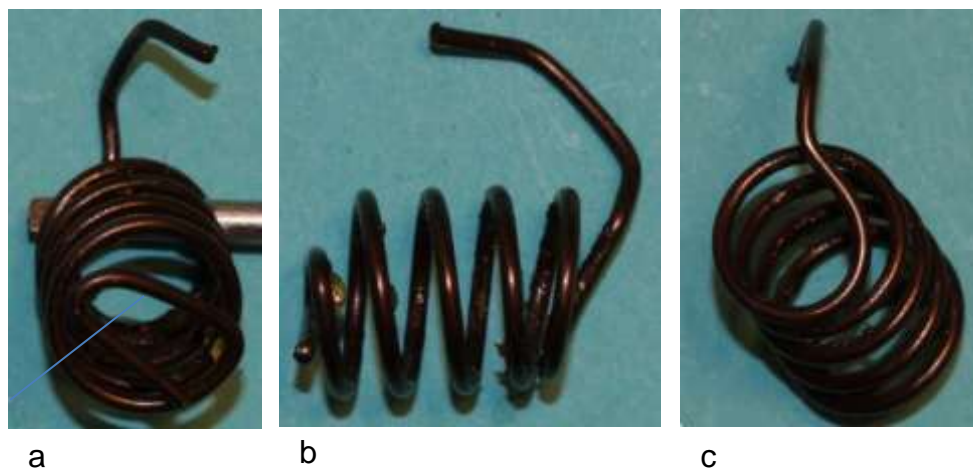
Druckfeder: a) Schlaufe für den Eingriff des Drehbolzens, b) Achsiale Ausdehnung der Druckfeder, c) Druckfederende zur Kontaktierung des unteren Klauenpolrings
